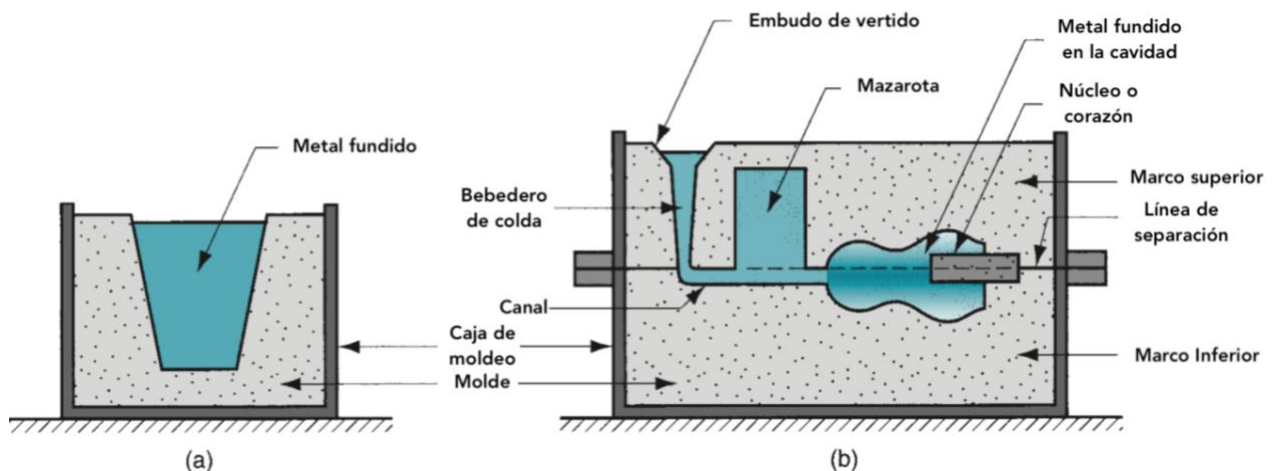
Representación esquemática del molde a) abierto, b) cerrado. Adaptado de [2].
